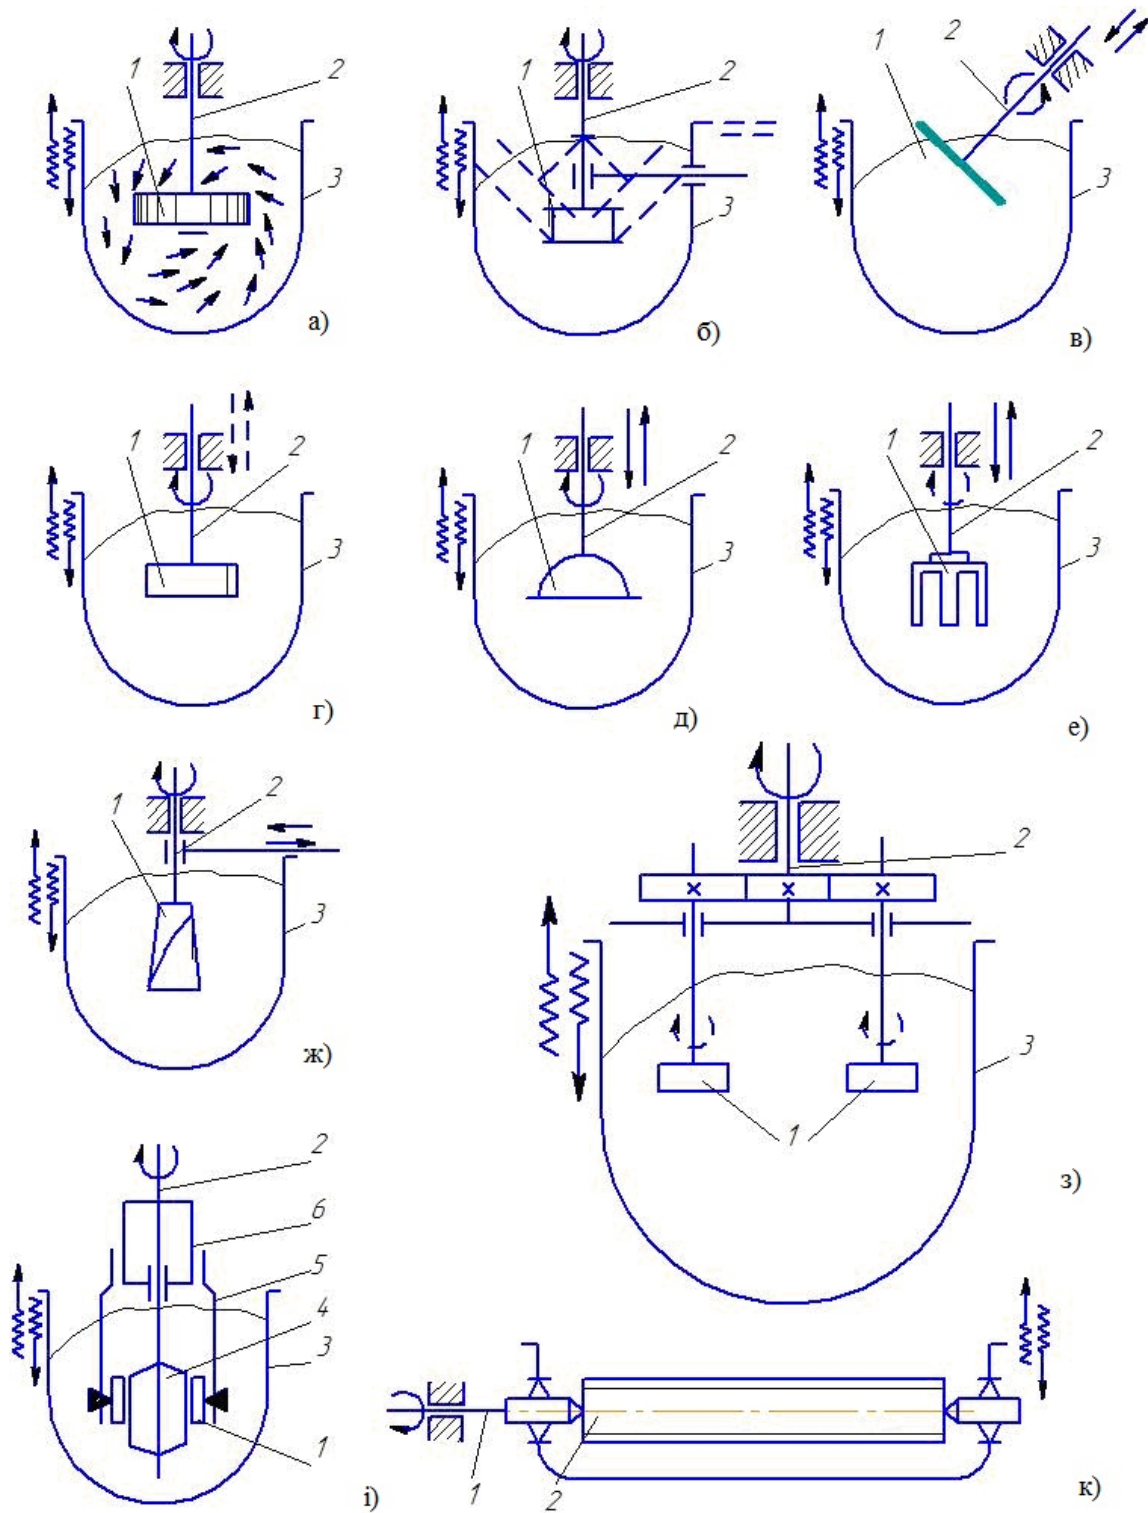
Схеми руху оброблюваної деталі при різних видах вібраційної шпиндельної обробки:
